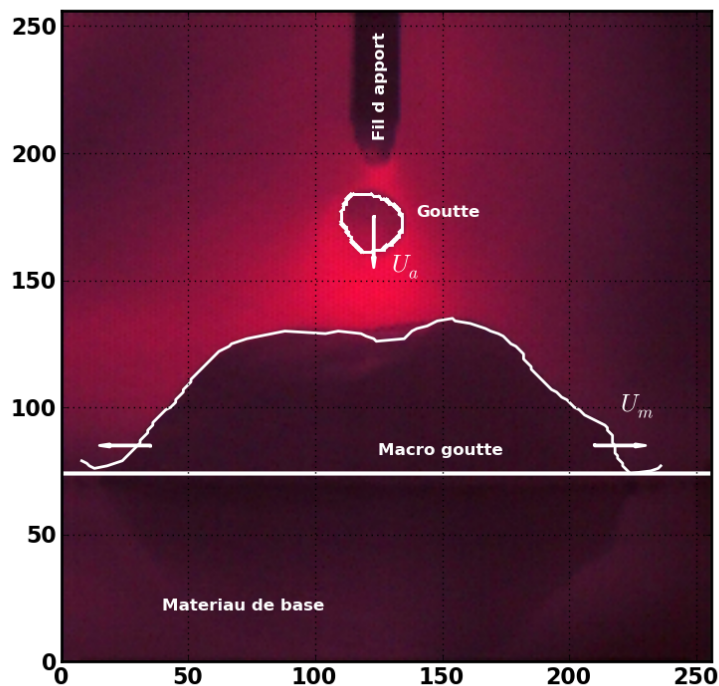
Description image macro-goutte en cours de soudage
